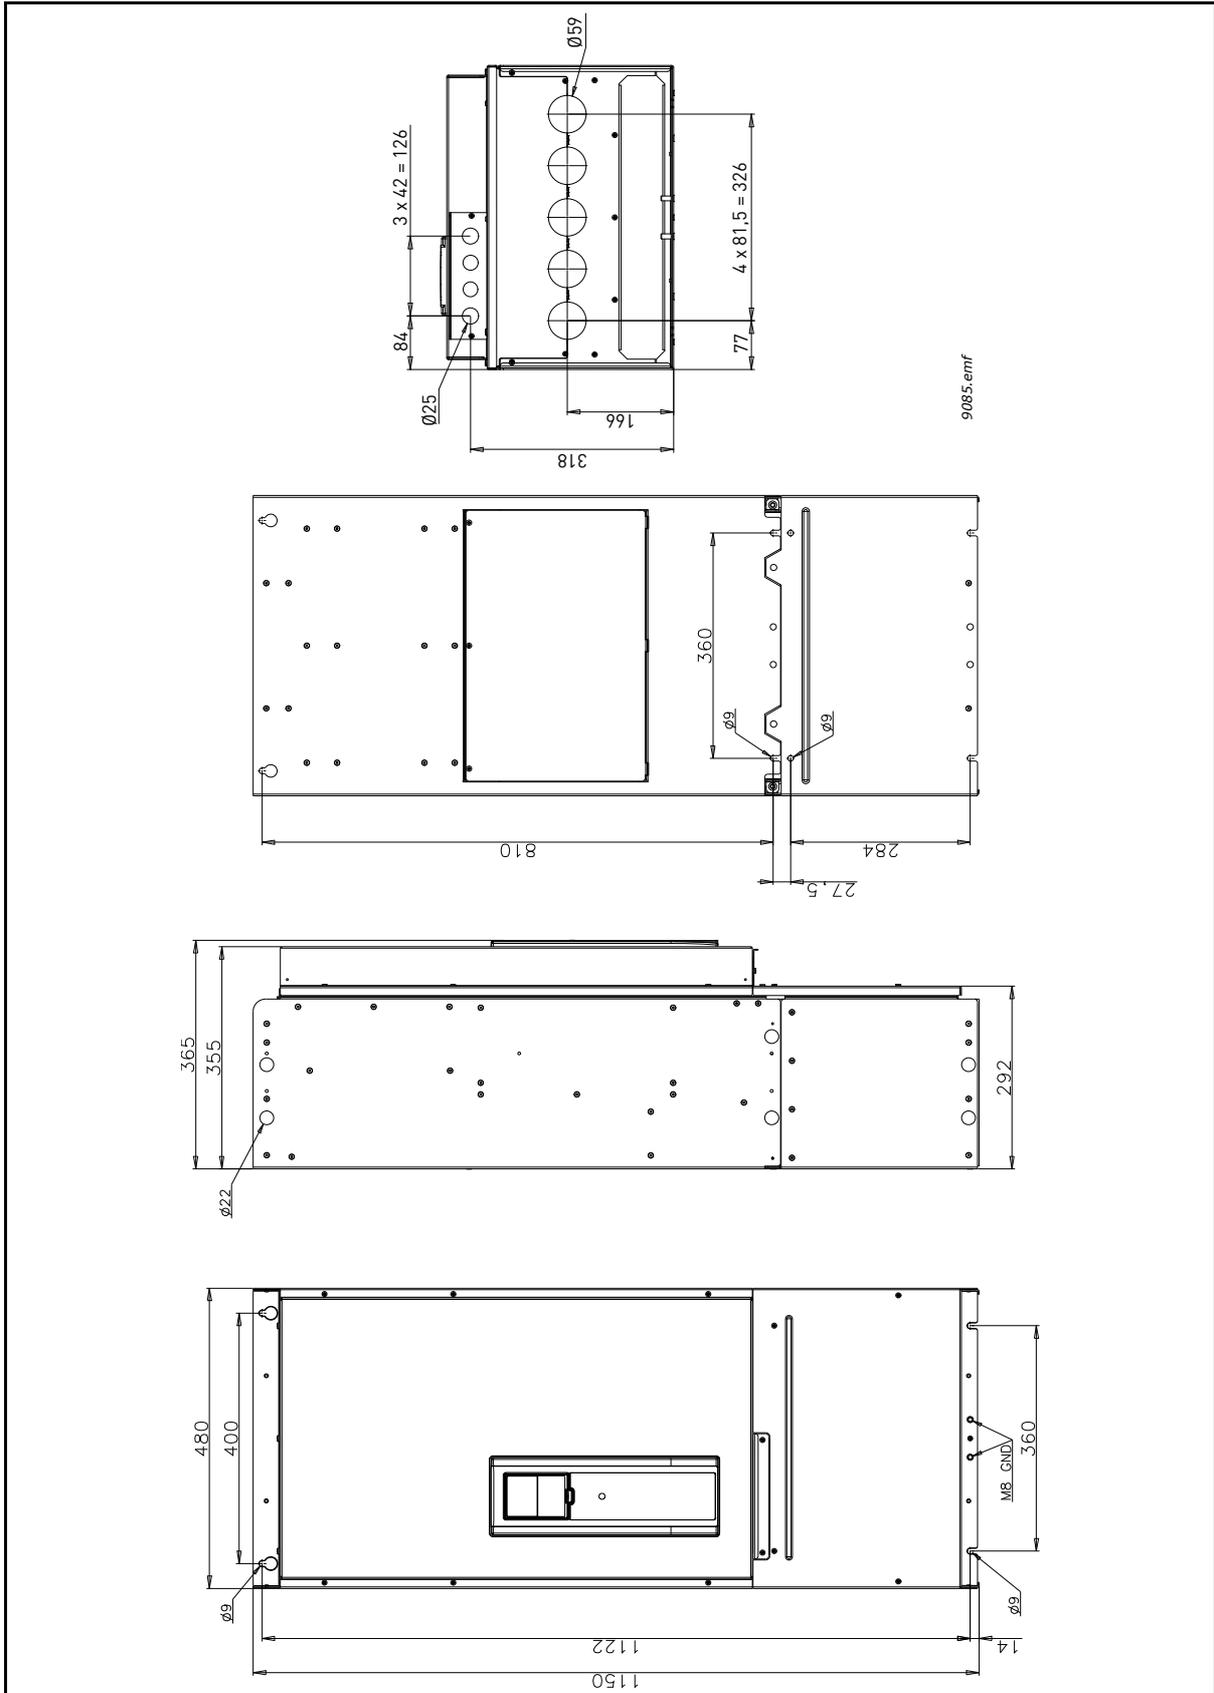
Dimensiones del variador de CA Vacon, MR9 IP21 y IP54
